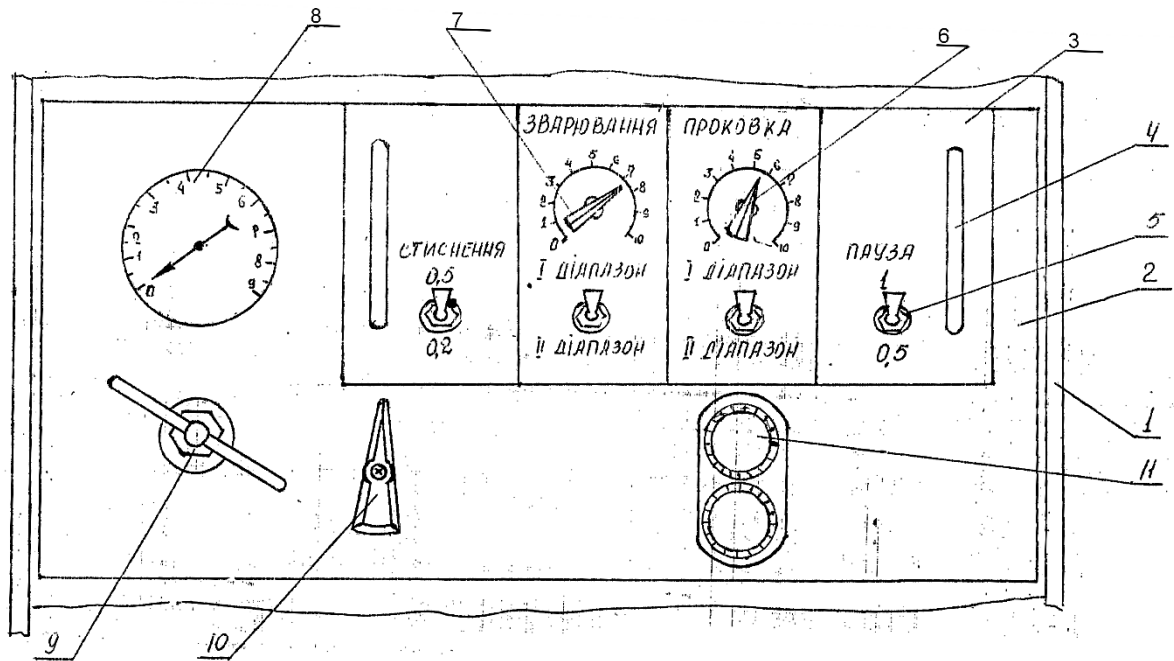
Акустичний пристрій для зварювання металів
